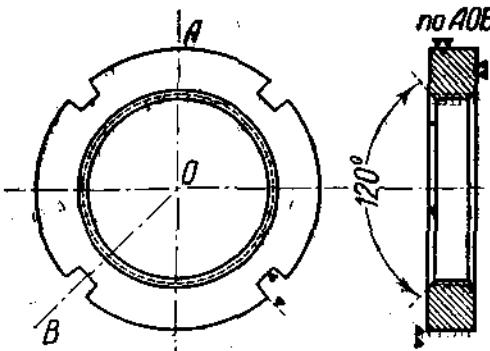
Гайка установочная фрезерованная с мелкой метрической резьбой.
